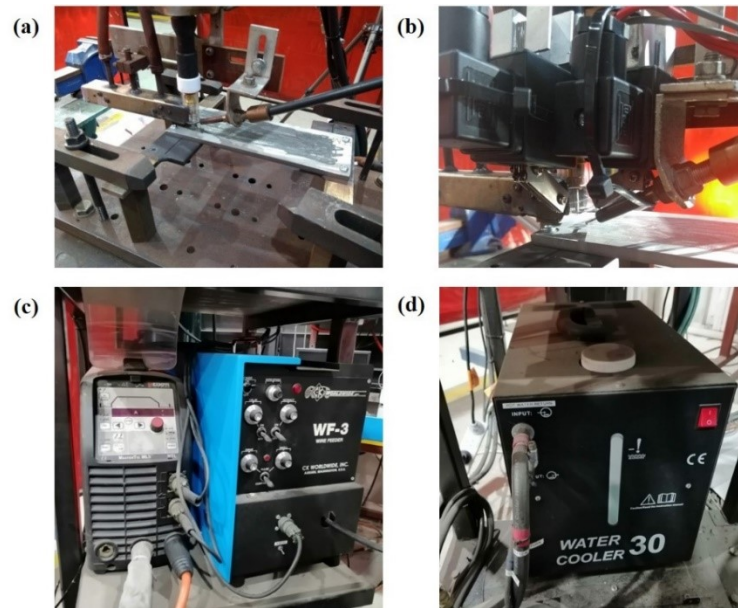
Sistema de manufatura aditiva baseada no processo GTAW da UOW. (a) Tocha GTAW e bico de saída do arame, (b) bobinas eletromagnéticas, (c) Fonte de Soldagem e Alimentador de Arame, (d) Sistema de refrigeração da Tocha GTAW
